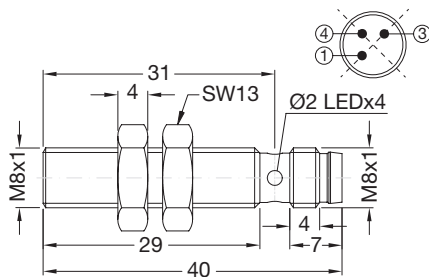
Kurze Ausführung, bündiger Einbau, Steckversion
